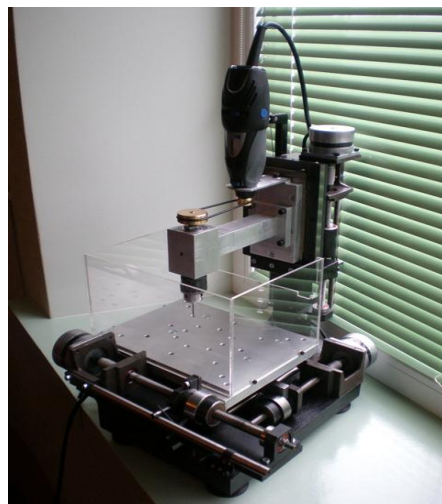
Настольный фрезерный станок с ЧПУ модульного принципа: вид спереди
